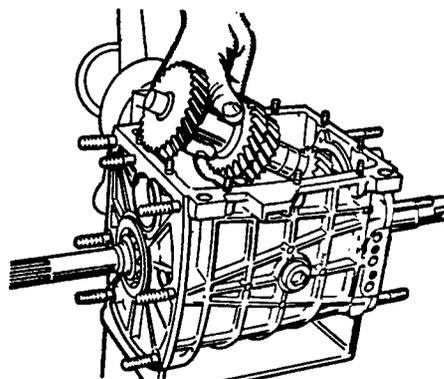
Извлечение промежуточного вала из картера коробки передач
